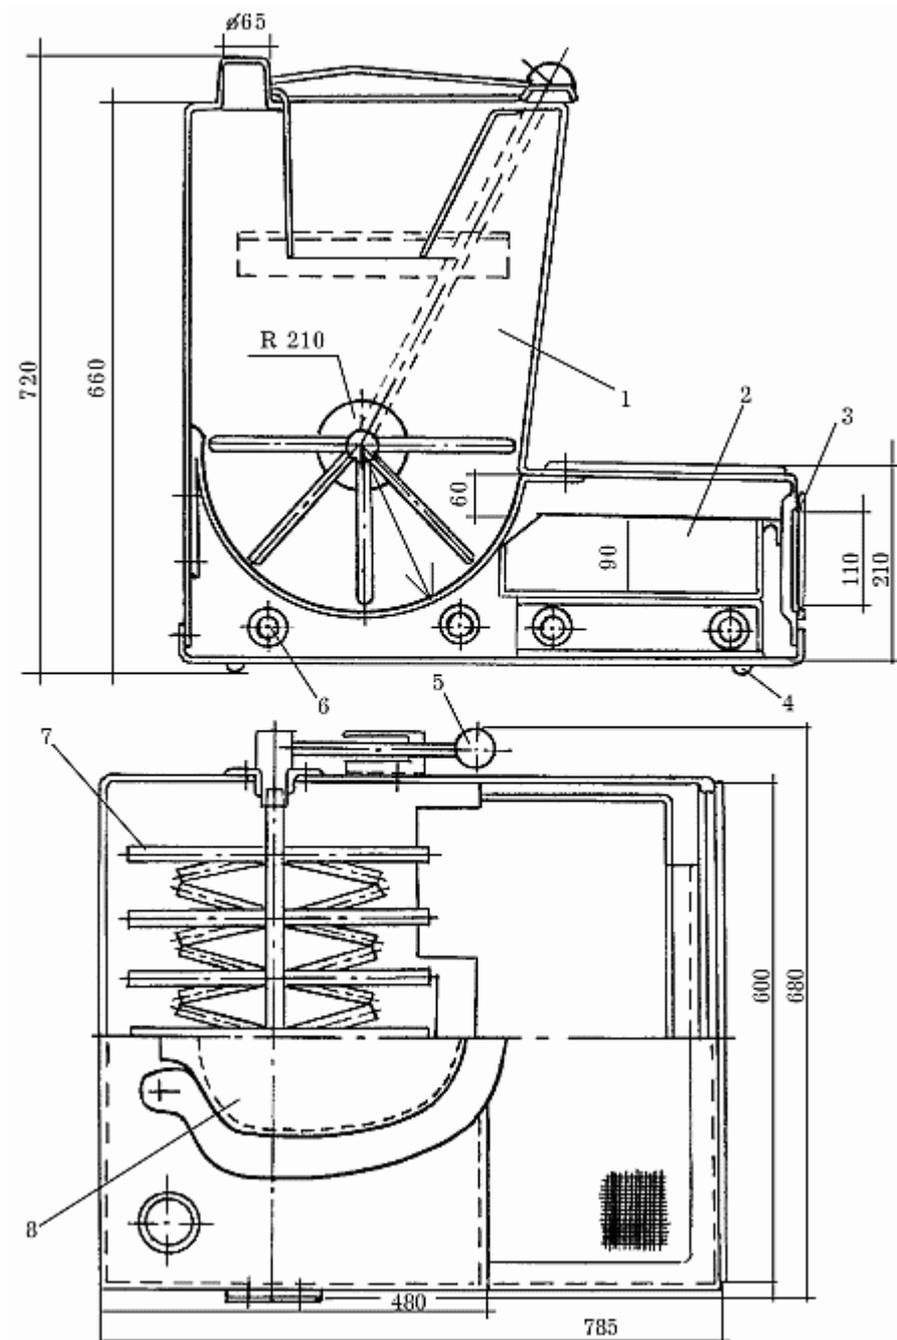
Биотуалет: 1 – корпус; 2 – ящик; 3 – лючок; 4 – основание; 5 – ручка; 6 – электронагреватель; 7 – рыхлитель; 8 – сиденье (размеры даны в мм).
